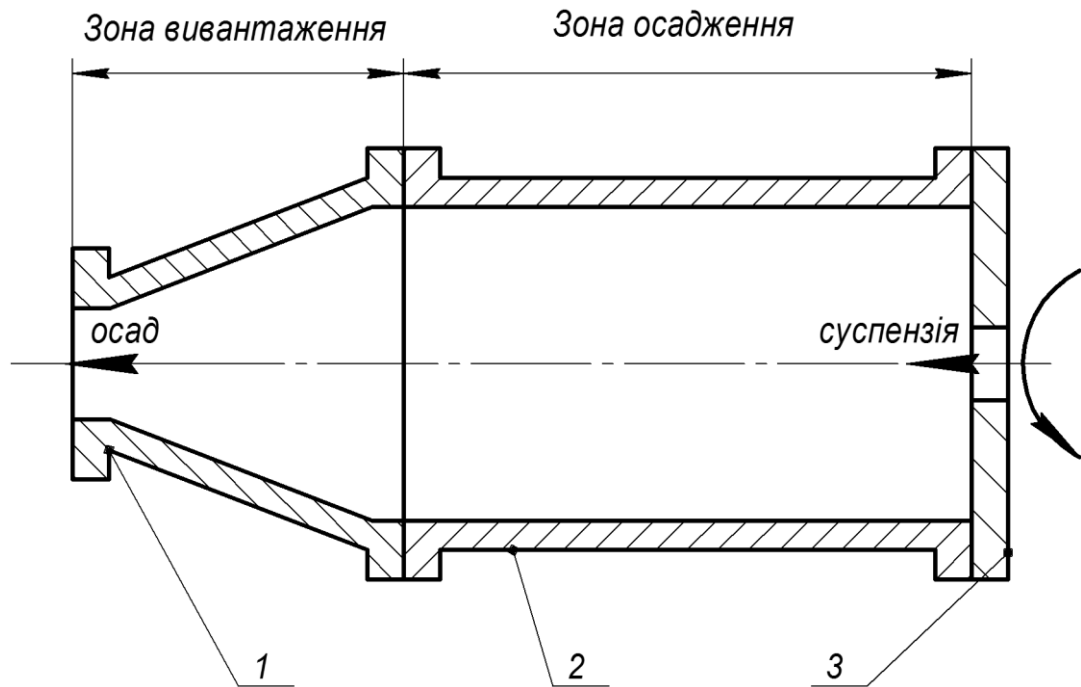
Схема ротора центрифуги марки ОГШ-352
